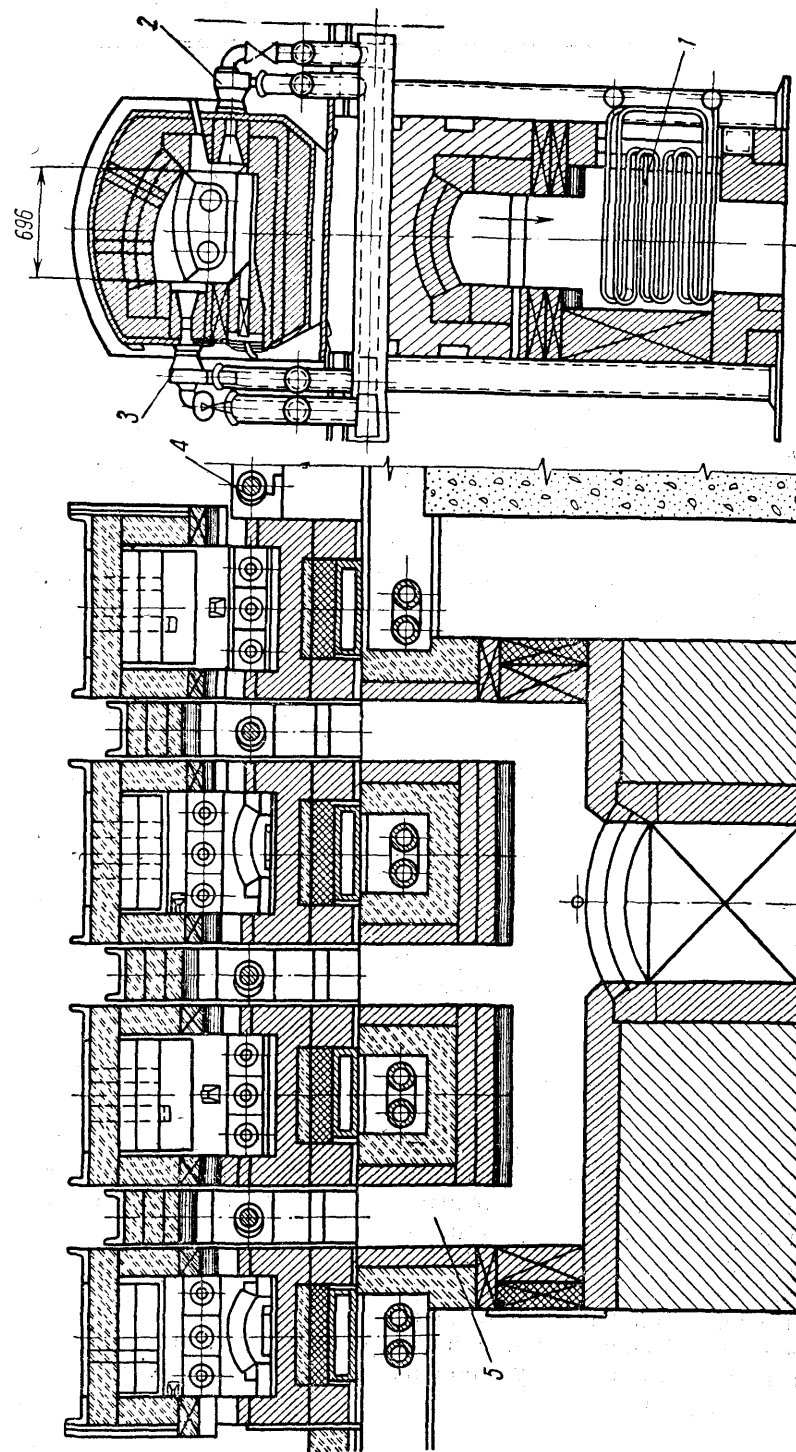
Секционная печь с нижним расположением рекуператоров для непрерывного скоростного нагрева круглых заготовок и труб: 1 — трубчатый рекуператор; 2 — нижняя двухпроводная газовая горелка; 3 — верхняя горелка; 4 — ролик для перемещения заготовок и труб; 5 — канал для отвода продуктов горения
